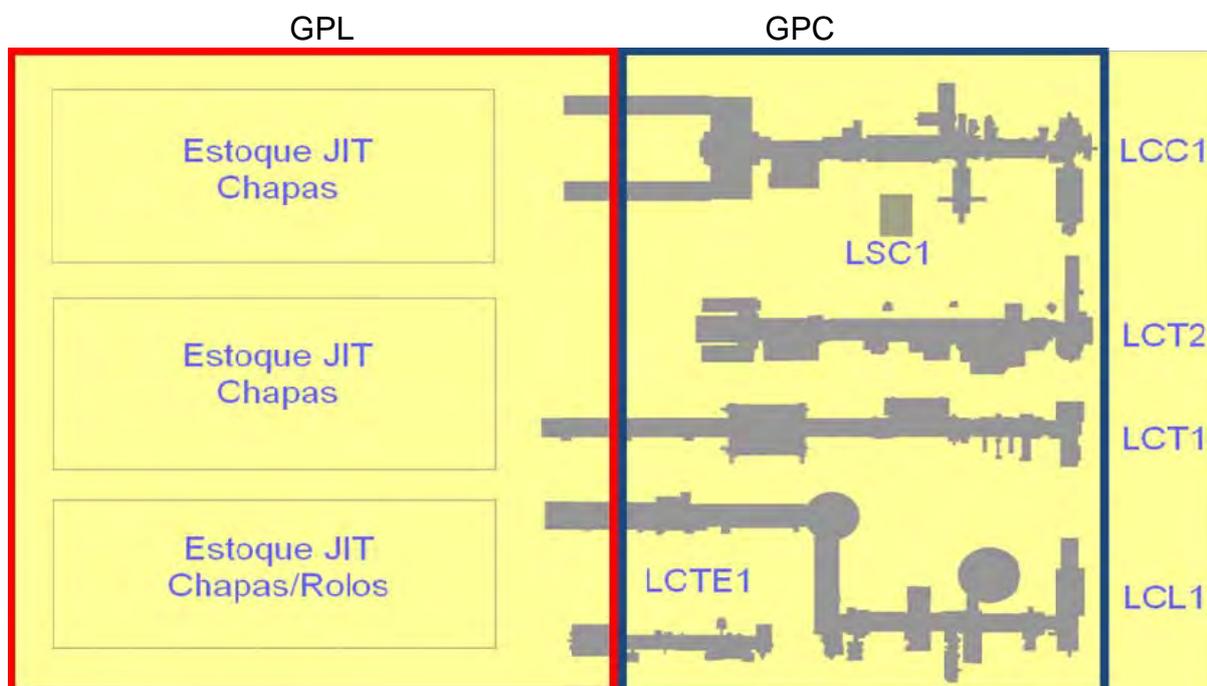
Planta CSN-PR – Centro de Serviços destacado em vermelho.
